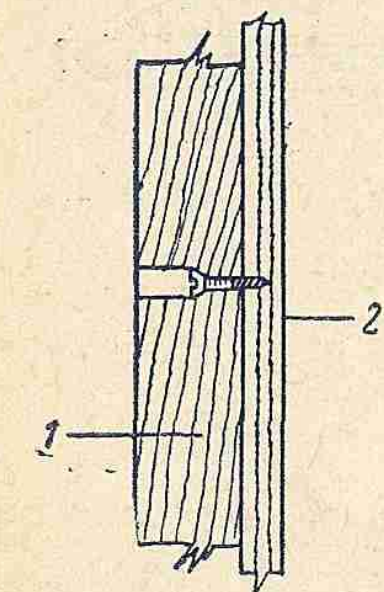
Способ крепления фанерных боковин корпусной мебели к деталям каркаса:
